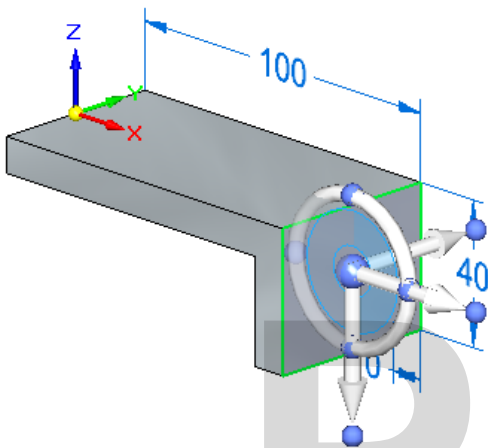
Das Steuerrad an einer Fläche des Bauteils
